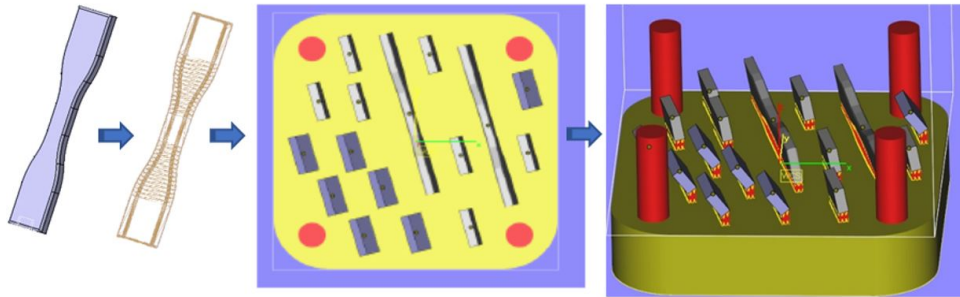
Plateau de fabrication des éprouvette FLLP en Inconel 625.
